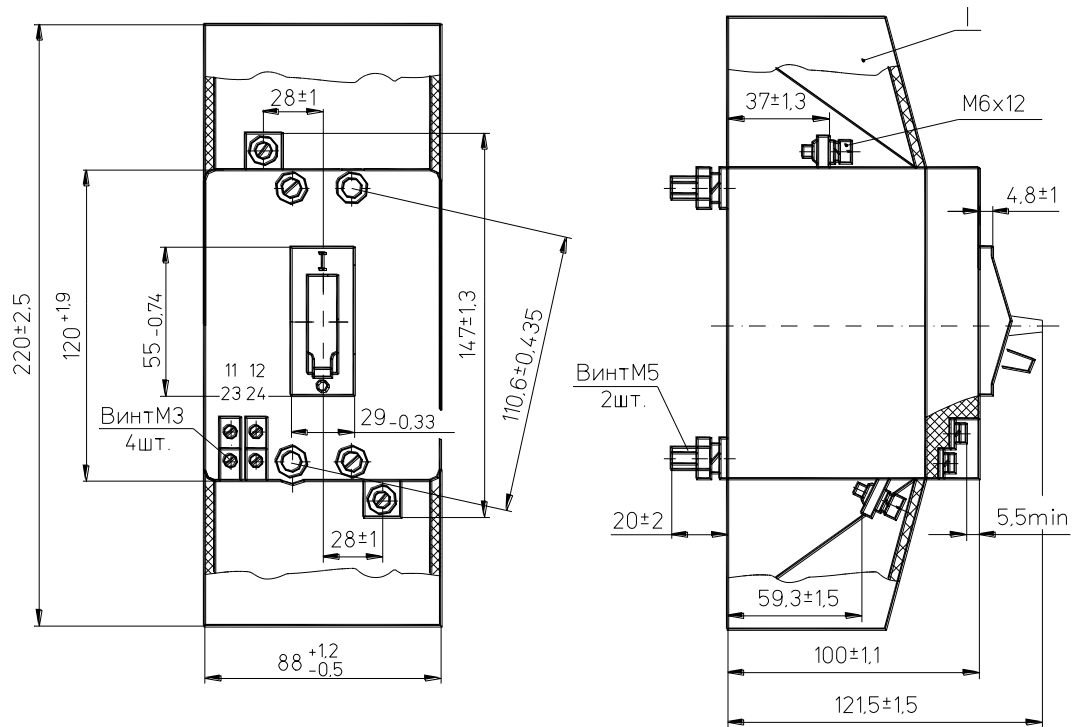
Сверление отверстий под винты крепления трехполюсного выключателя:
